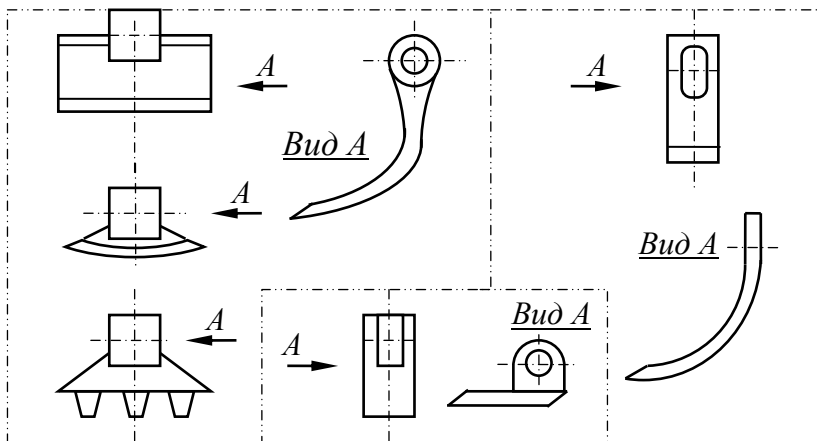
Ножи косилки-измельчителя с шарнирно закрепленными Г-образными ножами.
